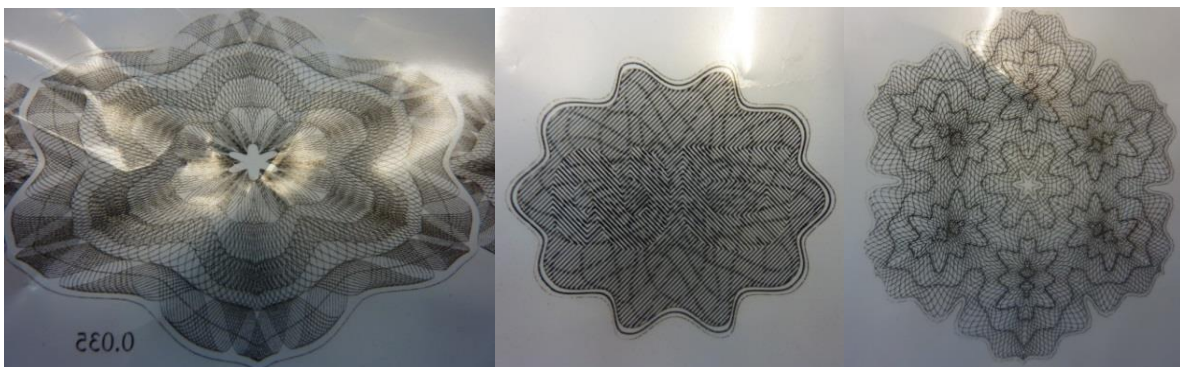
Gravierter Tiefdruckzylinder mit ns-Laser
